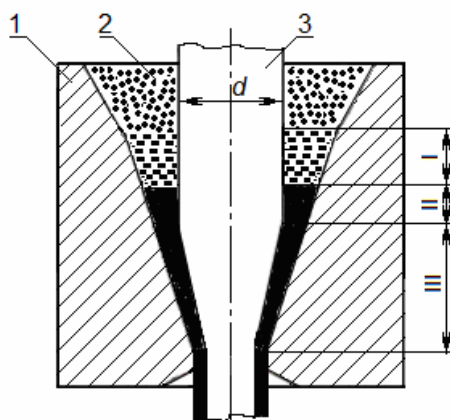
Схема формирования покрытия из порошка металла при волочении:
